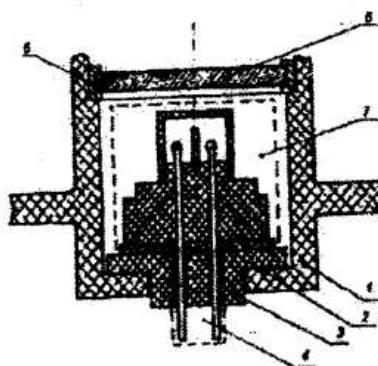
Конструкция датчика з двоєм газодиффузионним фільтром : 1- корпус изделия; 2 – амортизатор; 3 – втулка; 4 – датчик в сборе; 5 – кассета; 6 – фільтруючий елемент; 7 – порожність.
